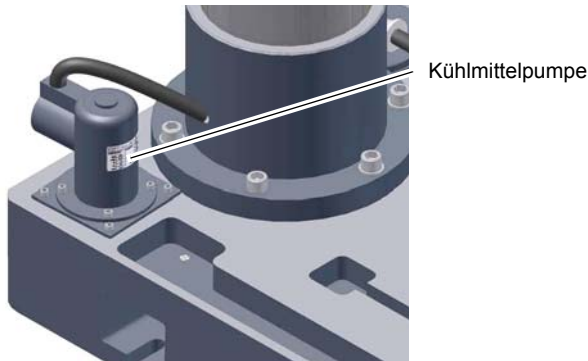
Kühlmittelpumpe Getriebebohrmaschine
